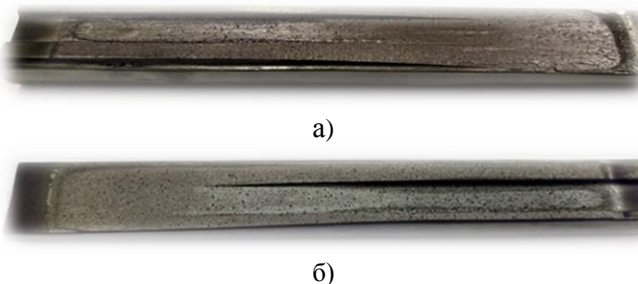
Внешний вид образцов перед проведением испытаний:
